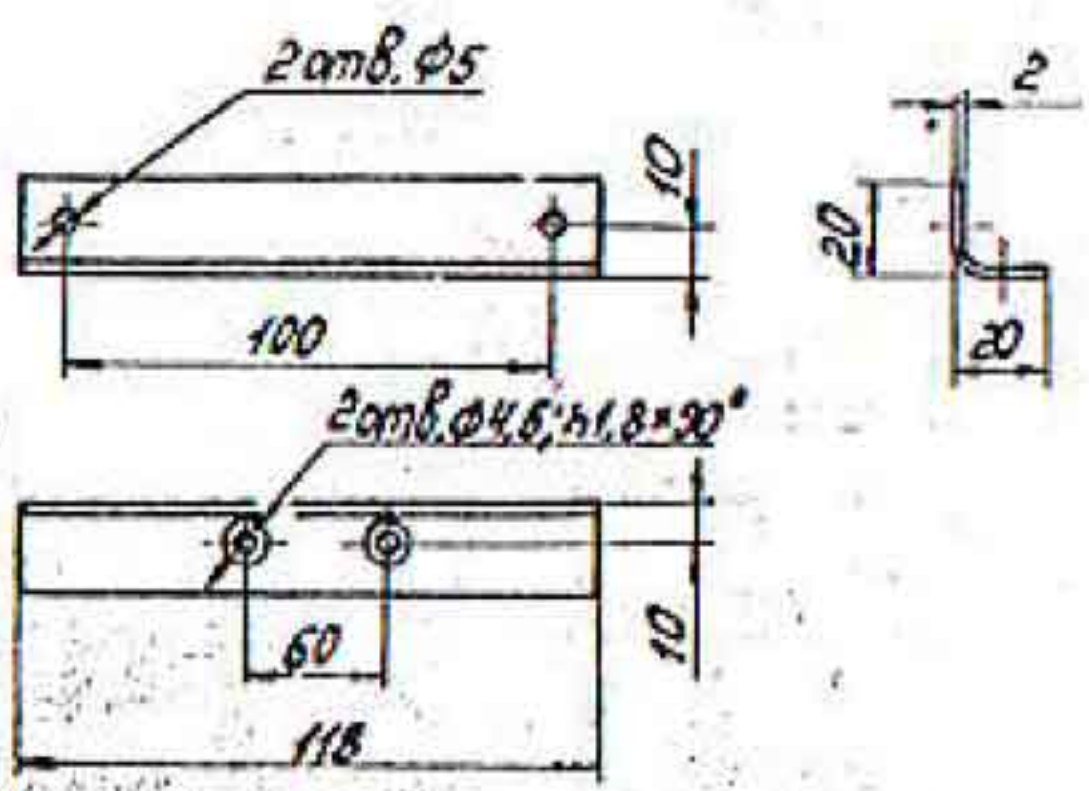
Эскиз детали для щитового крепления УЦН (гит)
